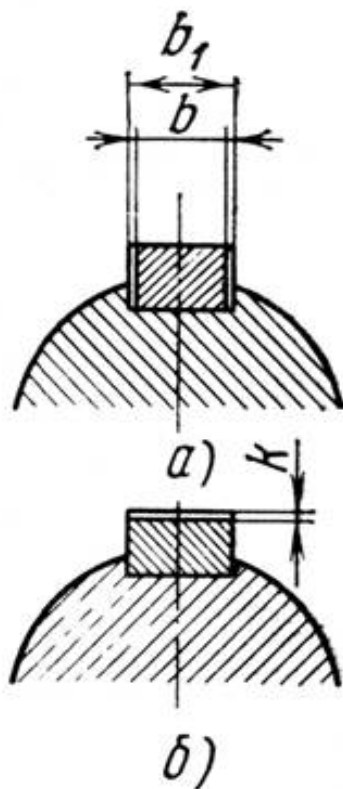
Соединения с клиновой (*а*) и призматической (*б*) шпонками
